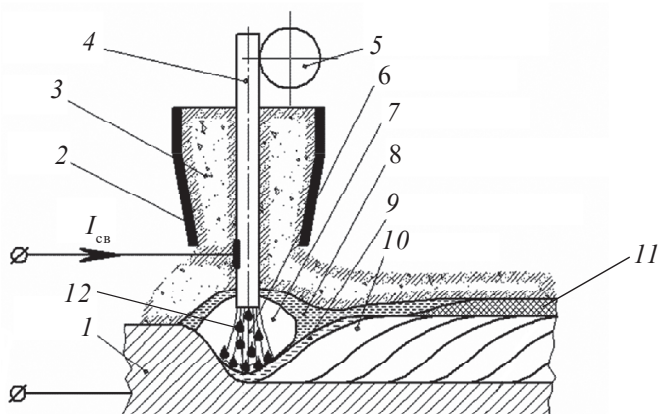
Автоматическая сварка под слоем флюса:
